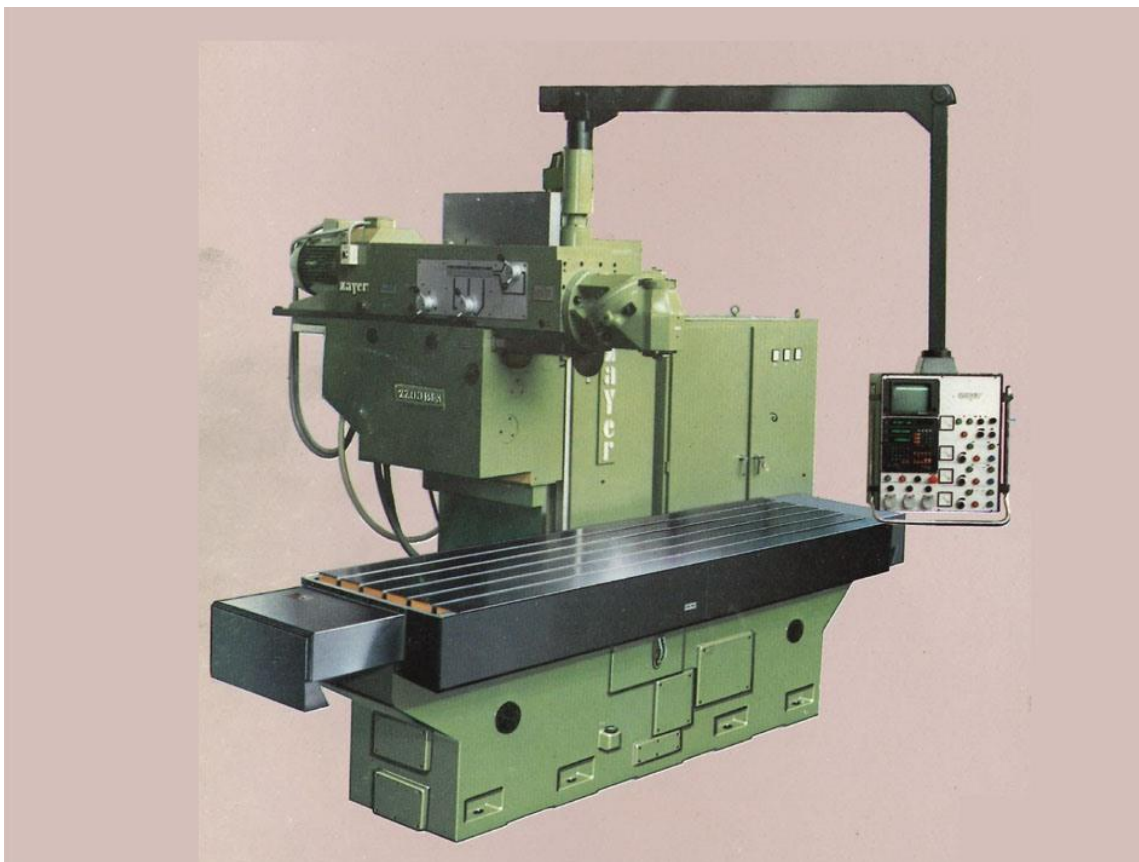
Загальний вигляд фрезерного верстата з поздовнім столом Zayer
